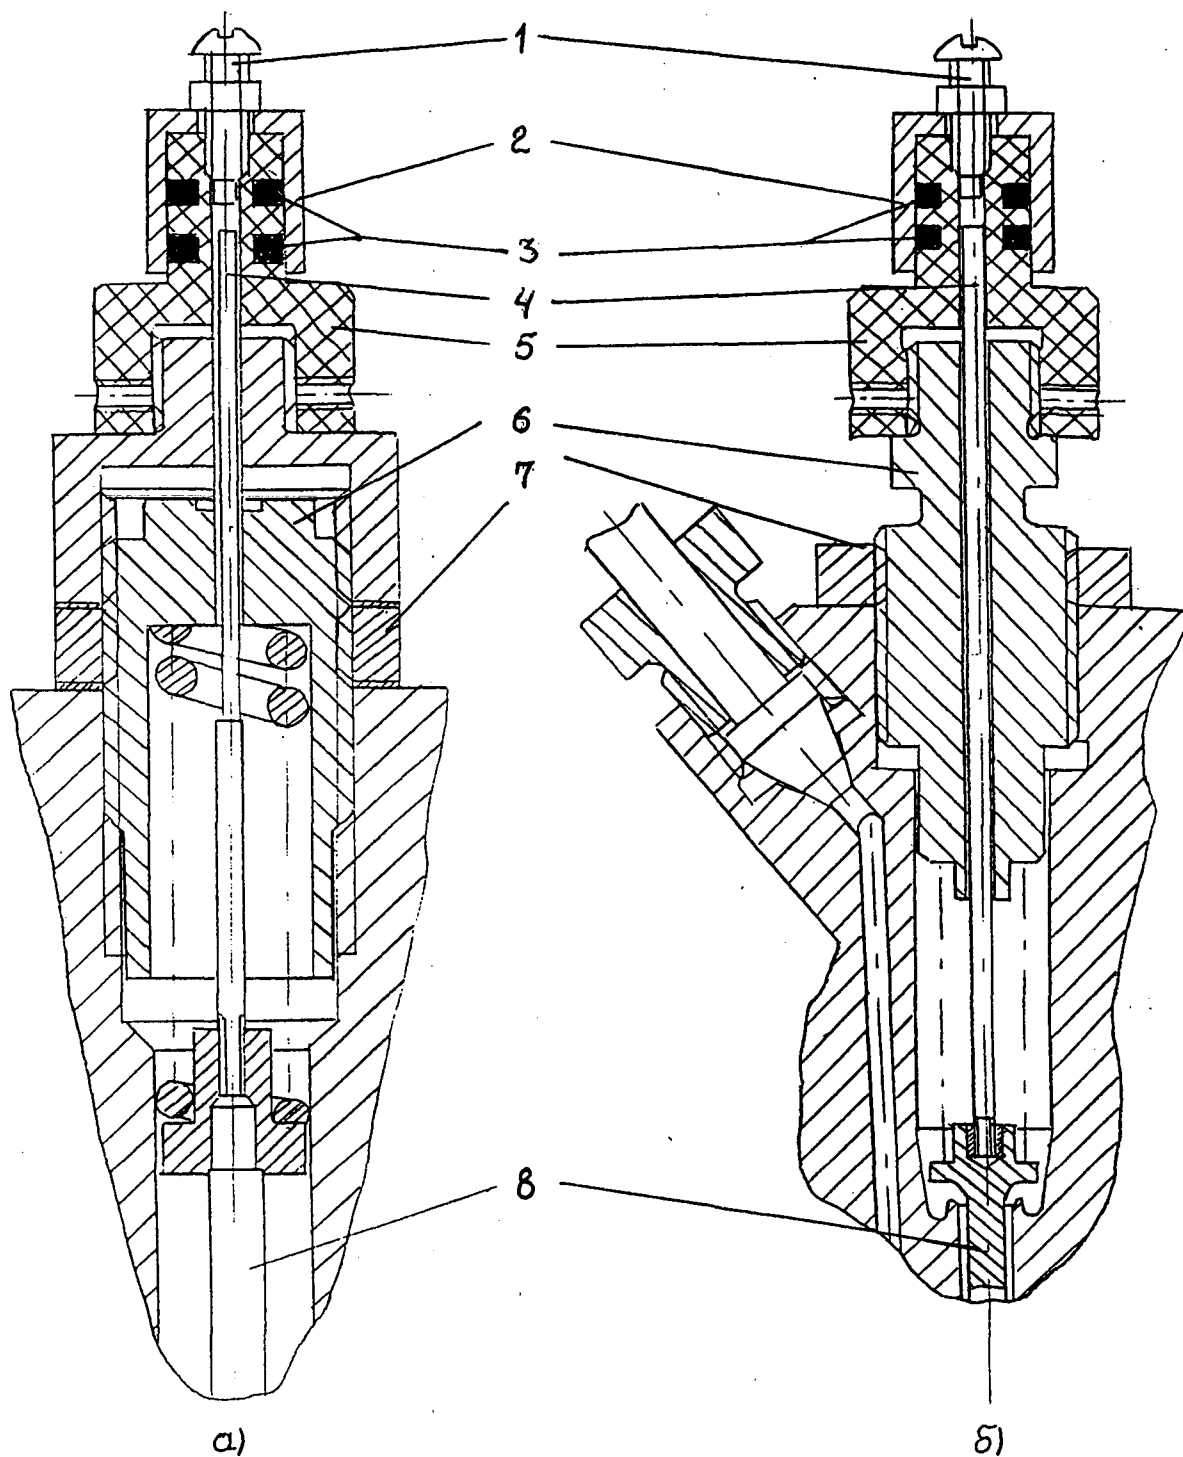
Конструкция и способы установки индуктивного датчика для измерения перемещения иглы форсунки дизеля: *а*- 6ЧН31/36; *б*- 6ЧН21/21: 1- регулировочный винт; 2- защитный кожух; 3- катушки; 4- стержень; 5- корпус датчика; 6- регулировочный винт пружины форсунки; 7- контргайка; 8- штанга.
